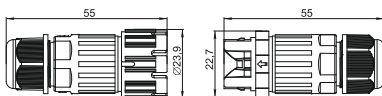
Габаритные размеры коннектора – WTP-204 /
